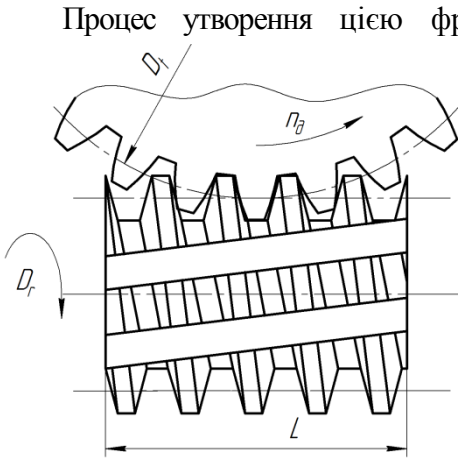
Схема роботи зубонарізної гребінчастої фрези з гвинтовою задньою поверхнею
